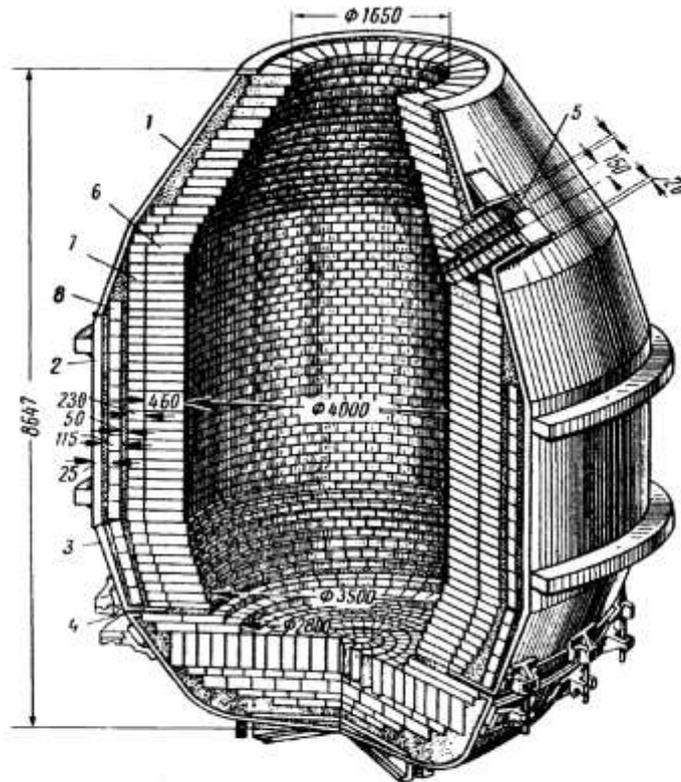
Корпус кисневого конвертера з футеровкою: 1 - шльомна частина; 2 - циліндричний пояс; 3 - нижній зрізаний конус; 4 - кільце; 5 - сталевипускний отвір; 6 - робочий шар футеровки; 7 - проміжний шар футеровки; 8 - арматурний шар
